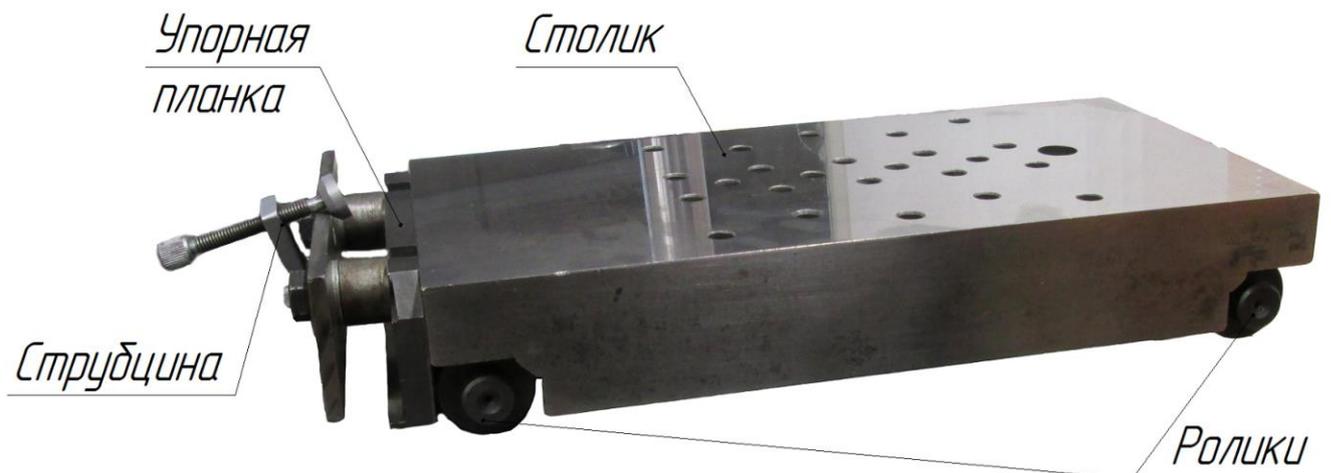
Конструкция синусной линейки для измерений калибров с фланцем
